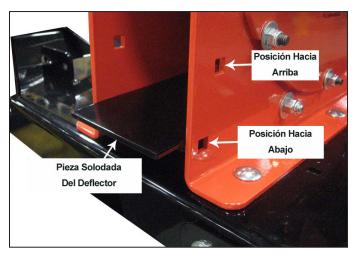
Pieza soldada del deflector de la chipeadora
